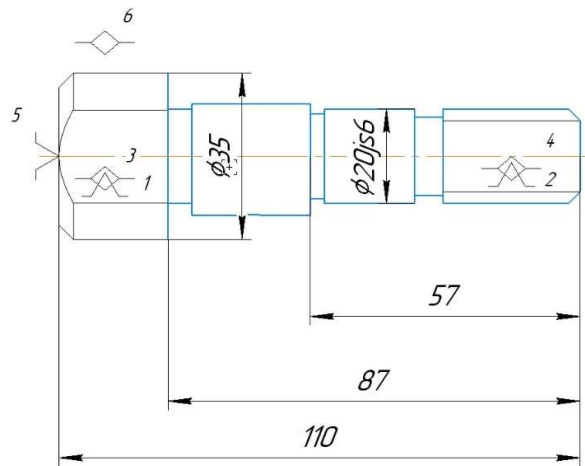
Базування деталі при токарній обробці по лівому торцю
